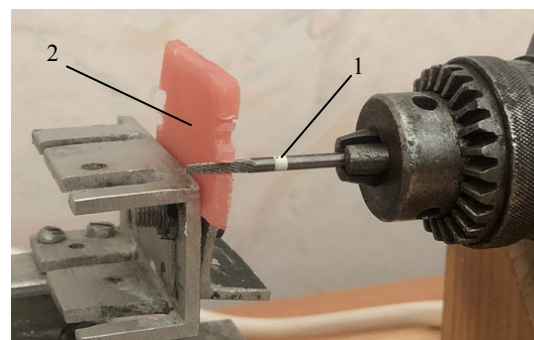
Фотография положения испытуемой фрезы относительно обрабатываемого образца
